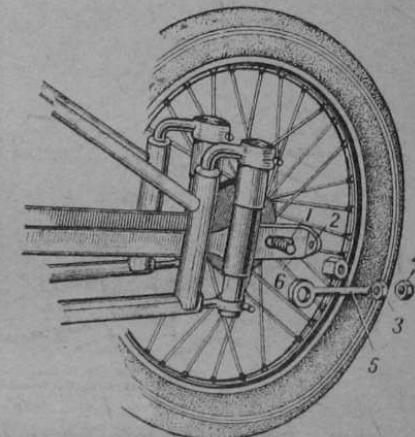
Натяжное устройство для цепи главной передачи ИЖ-49:
